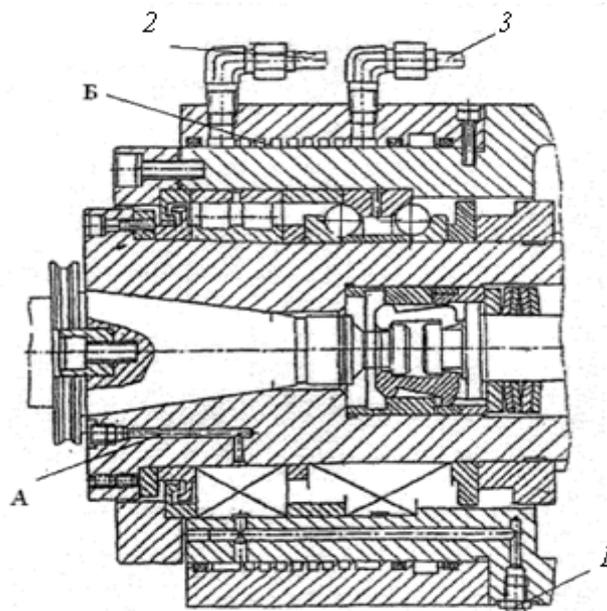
Шпиндельный узел многоцелевого фрезерно-сверлильно-расточного станка
